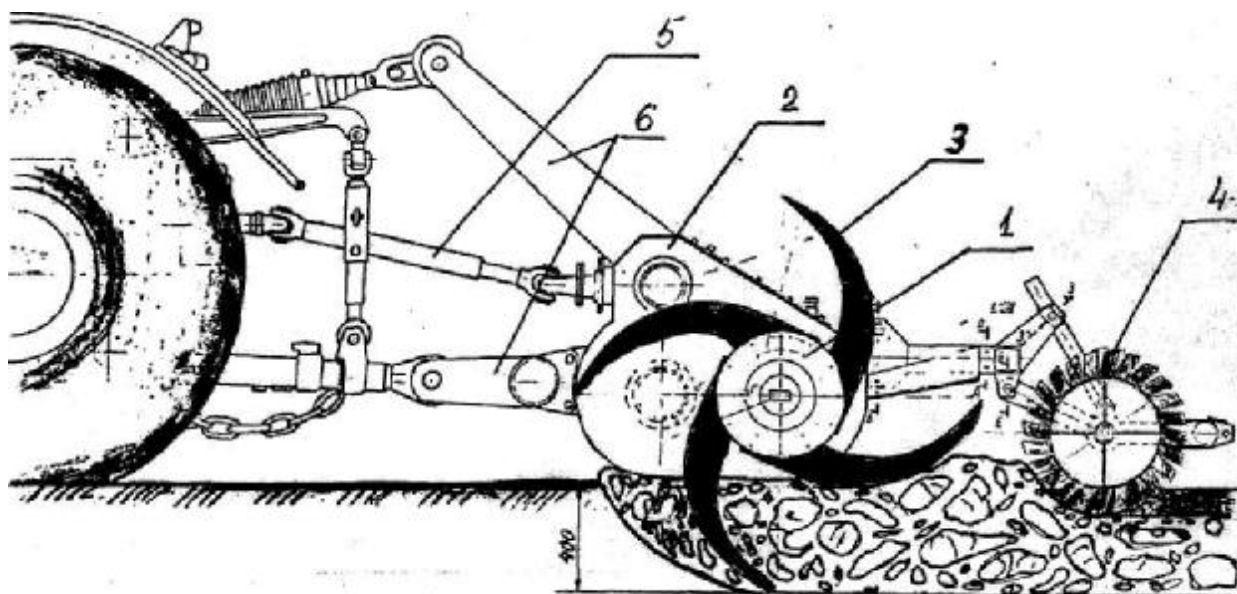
Схема роторного плуга – рыхлителя РПР – 2,4:
